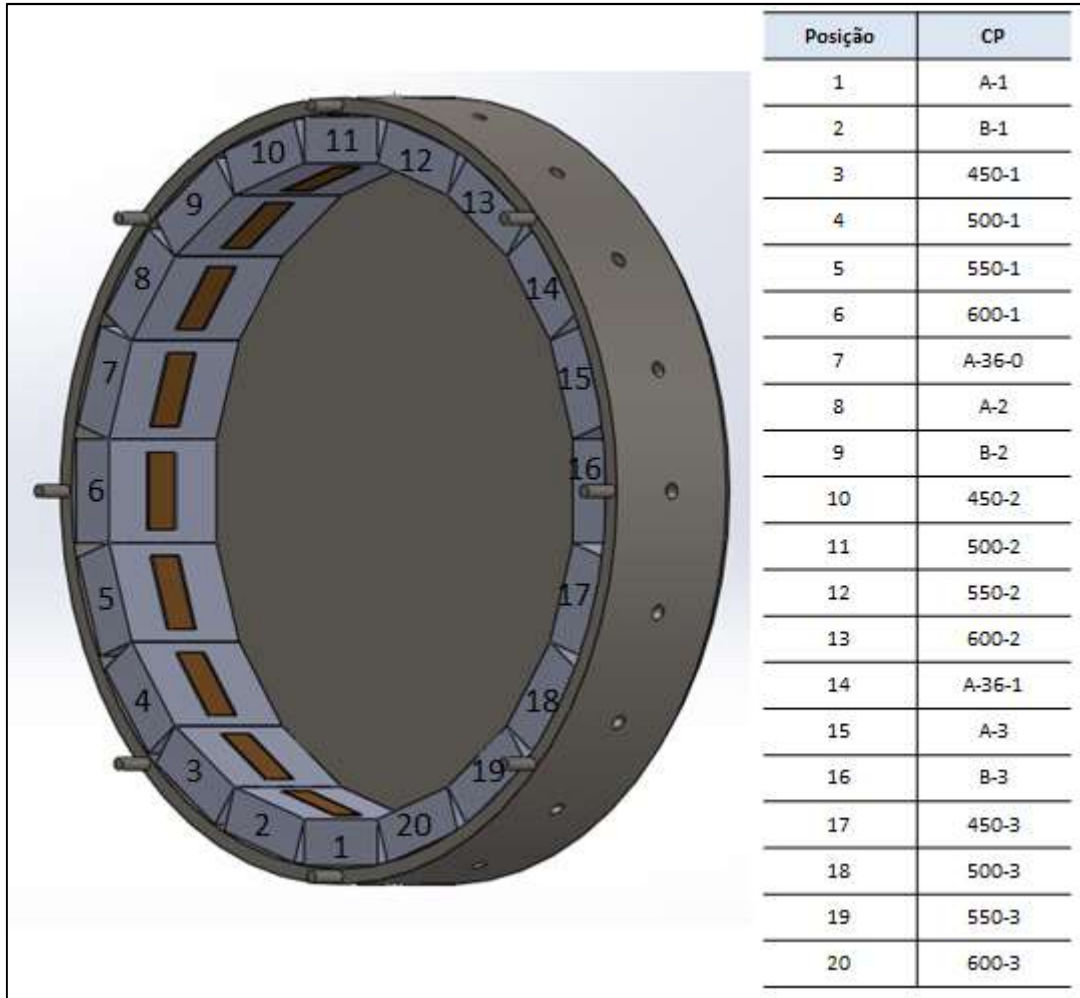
Posicionamento dos conjuntos dentro do tambor do abrasômetro.
